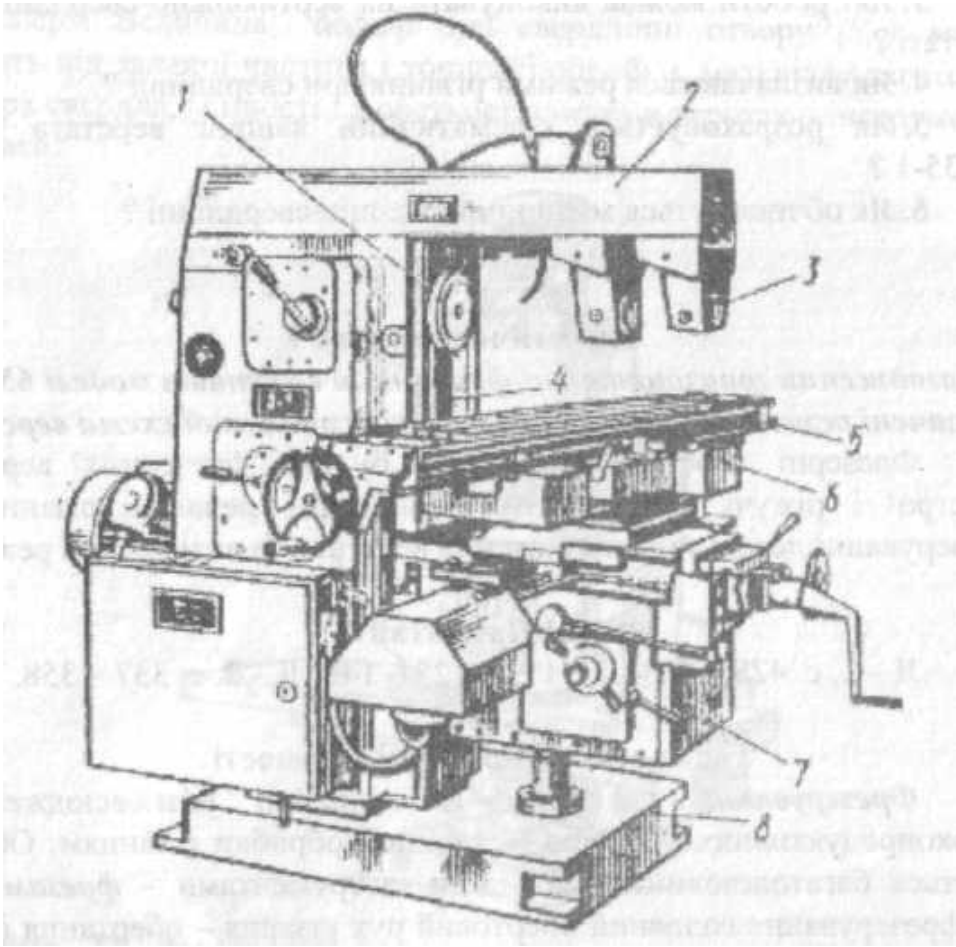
Загальний вигляд консольного горизонтально-фрезерного верстата моделі 6М82: 1 - шпindel; 2 - хобот; 3 - підвіска; 4 - станина; 5 — стіл; 6 — каретка; 7 — консоль; 8 - фундаментна плита
